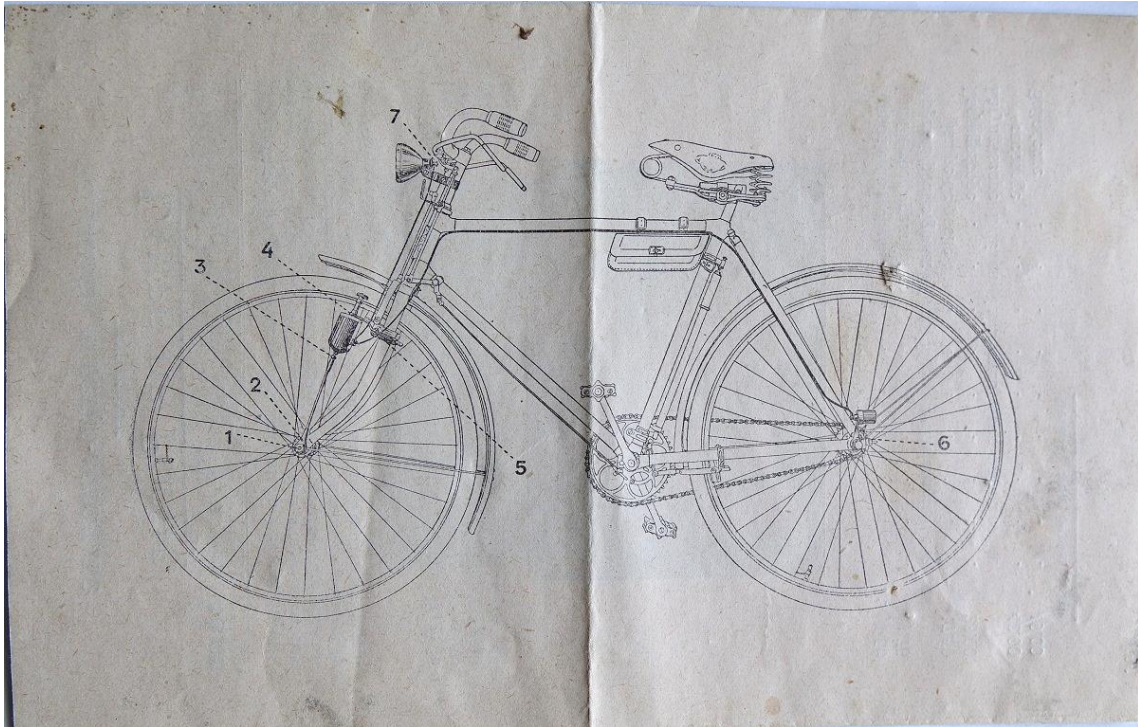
Rückseite des Beipackzettels im Bild 3.16
